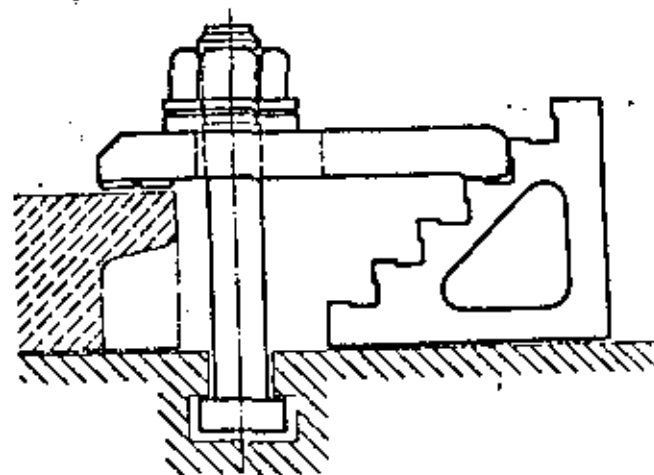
Tensor plano con soporte escalonado DIN 6110
